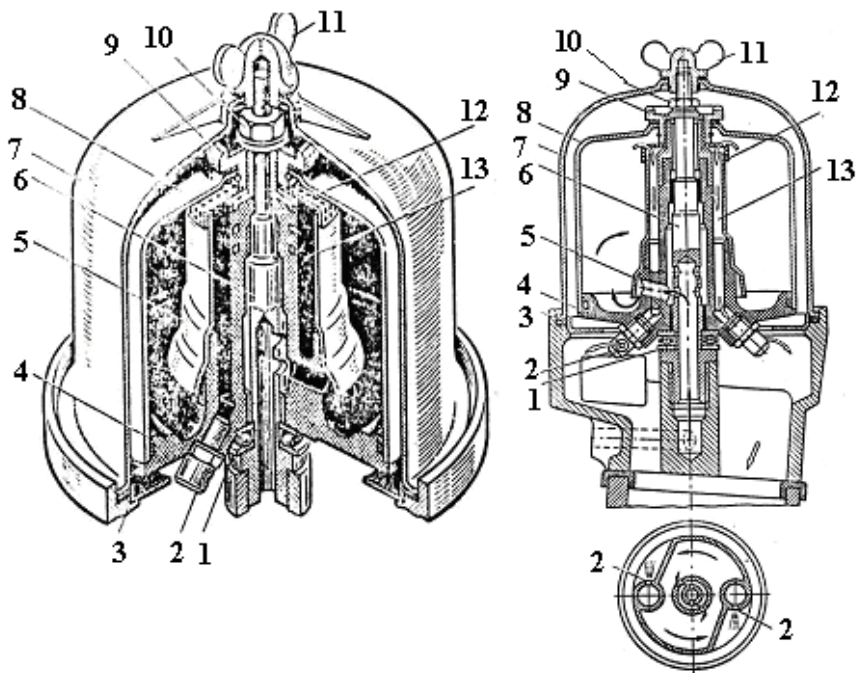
Неповнопоточний центробіжний очищувач оливи
